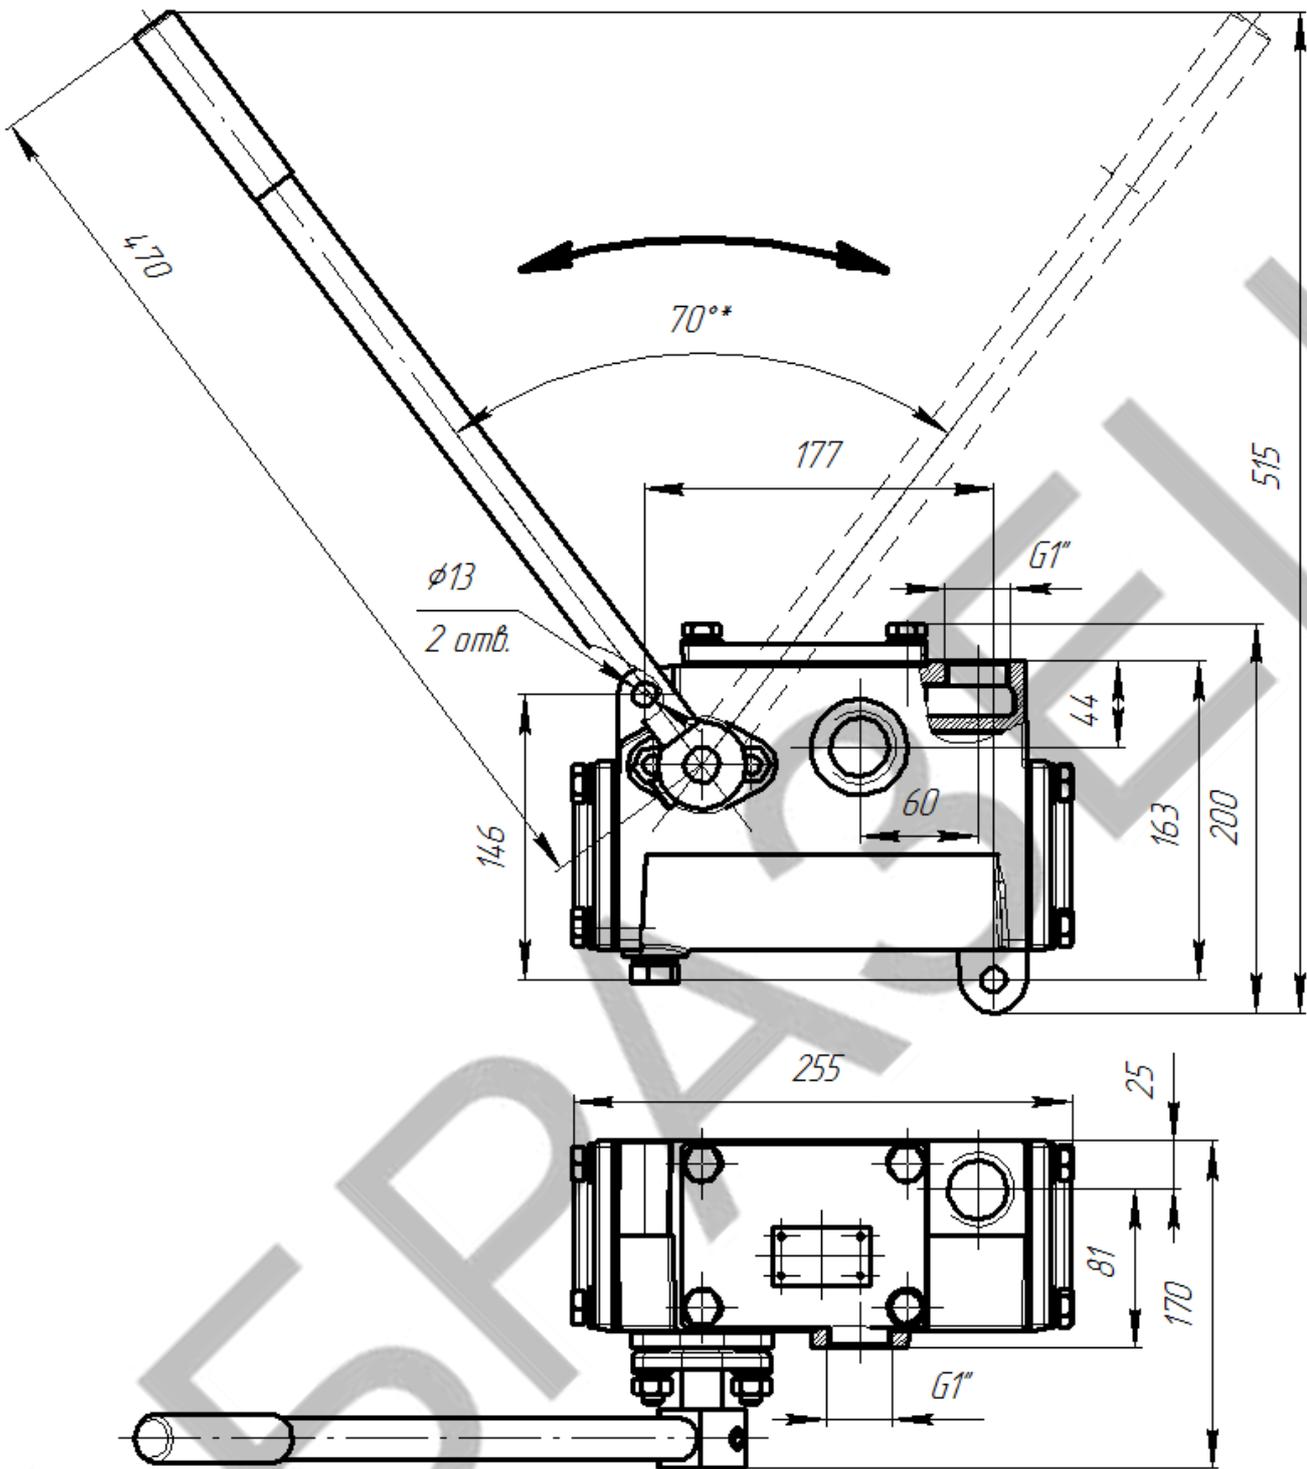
Габаритный чертеж насоса P-0,8/30.
